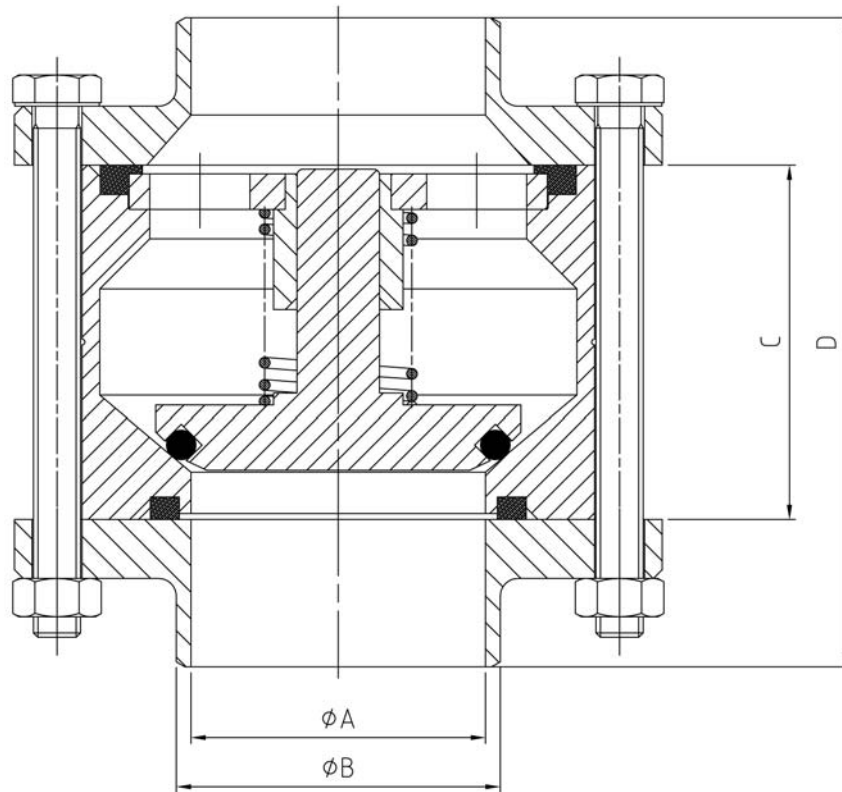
Abmessungen Tellerrückschlagventil DIN ZF
